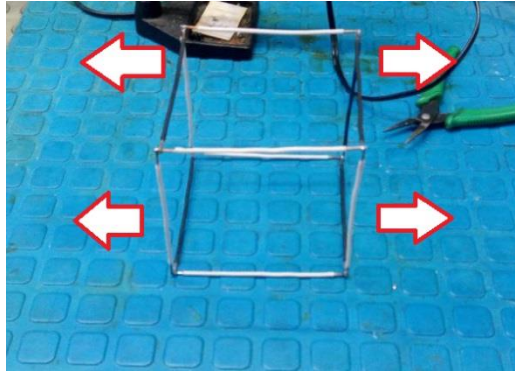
Ejemplo de prueba de soldadura – Autoría propia
